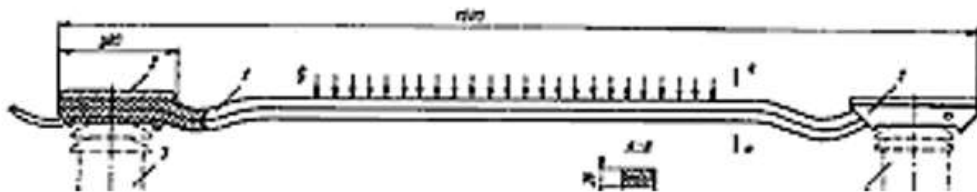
Конструкція ресорного склопластикового профілю: 1 – склопластикові пластини; 2 – металічні опори; 3 – головка стійки
